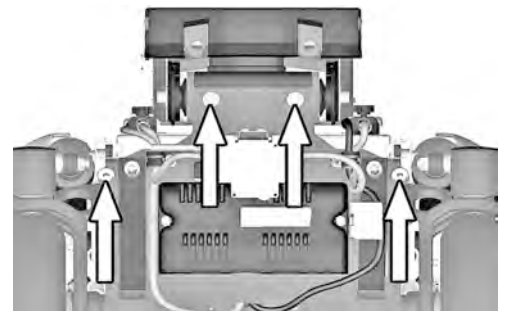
Der Batteriekasten ist mit vier Schrauben befestigt.
